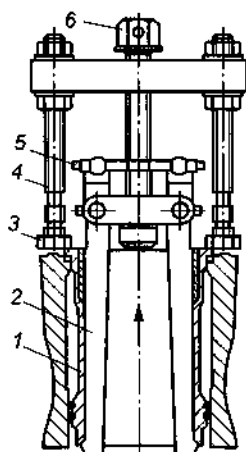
Комбинированный съемник для выпрессовки гильзы из блока цилиндров: 1 — гильза; 2 — лапки; 3 — гайка; 4 — шпилька; 5 — болт; 6 — винт
